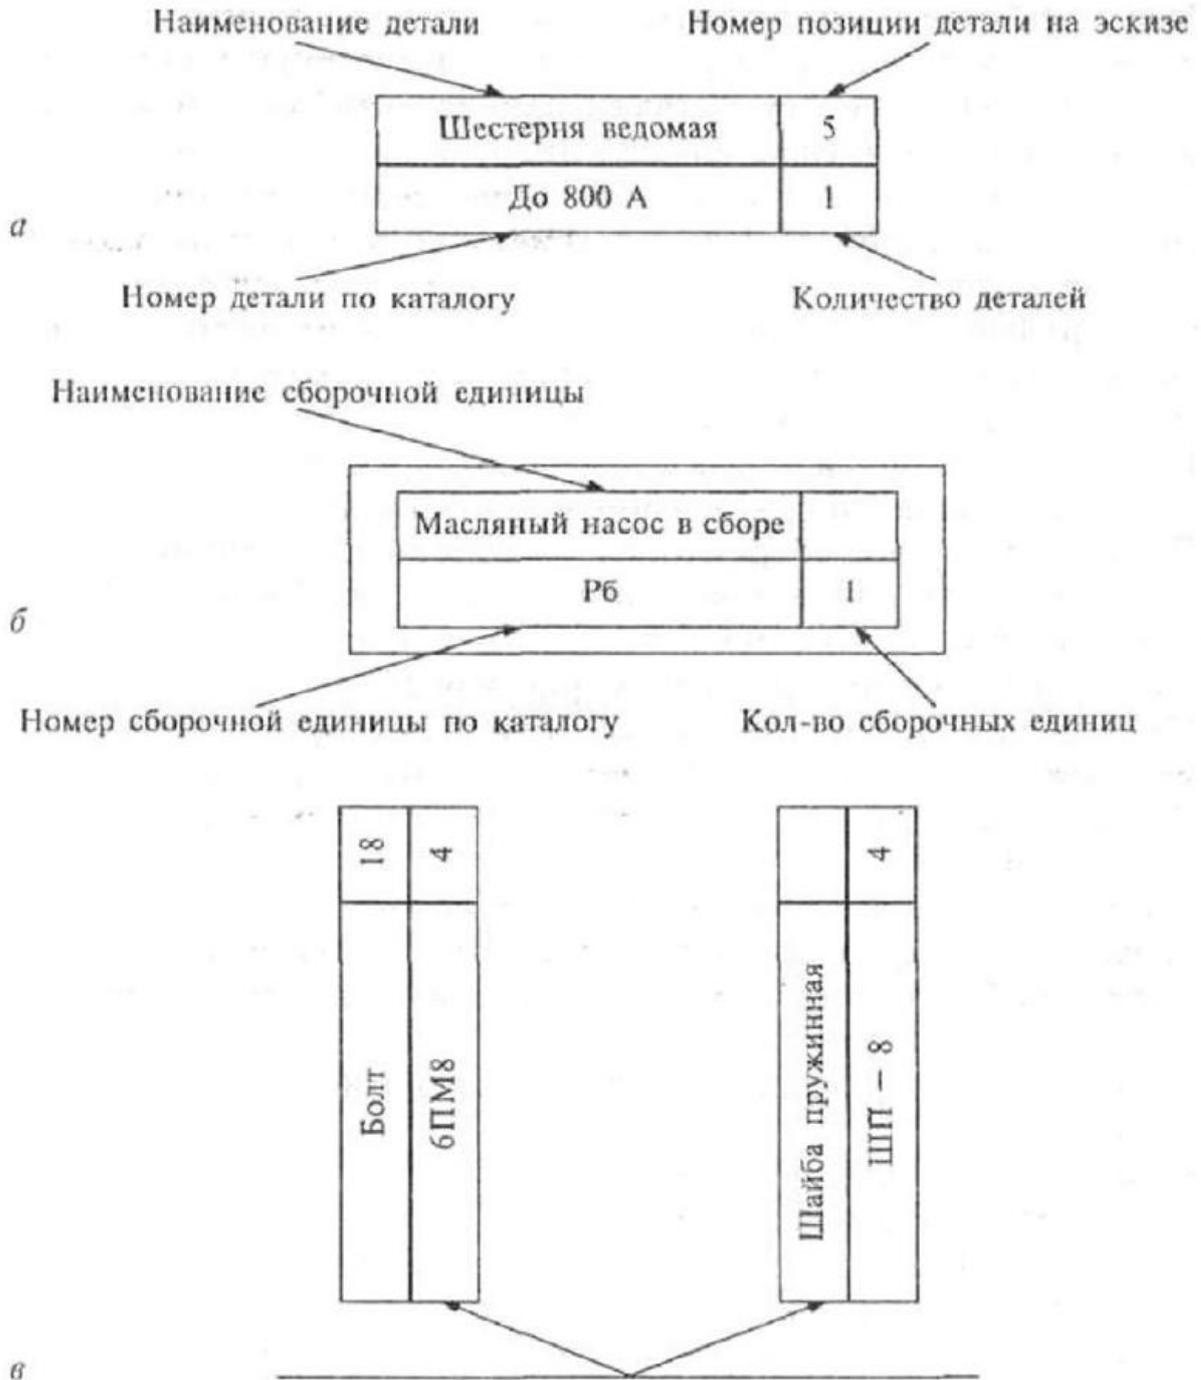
Условное обозначение на схеме разборки сборки:
